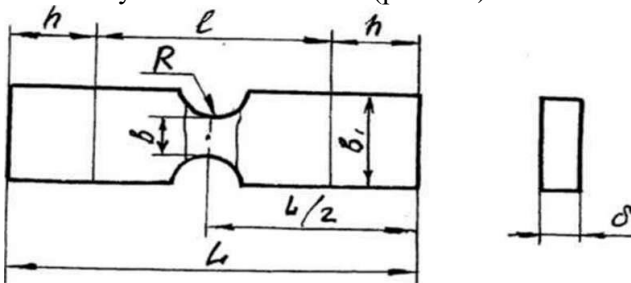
Зразки для випробування міцності шва стикового з'єднання
